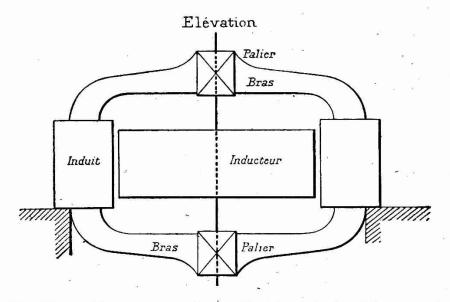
Alternateur à arbre vertical (type horizontal renversé). Coupe par un plan axial.
